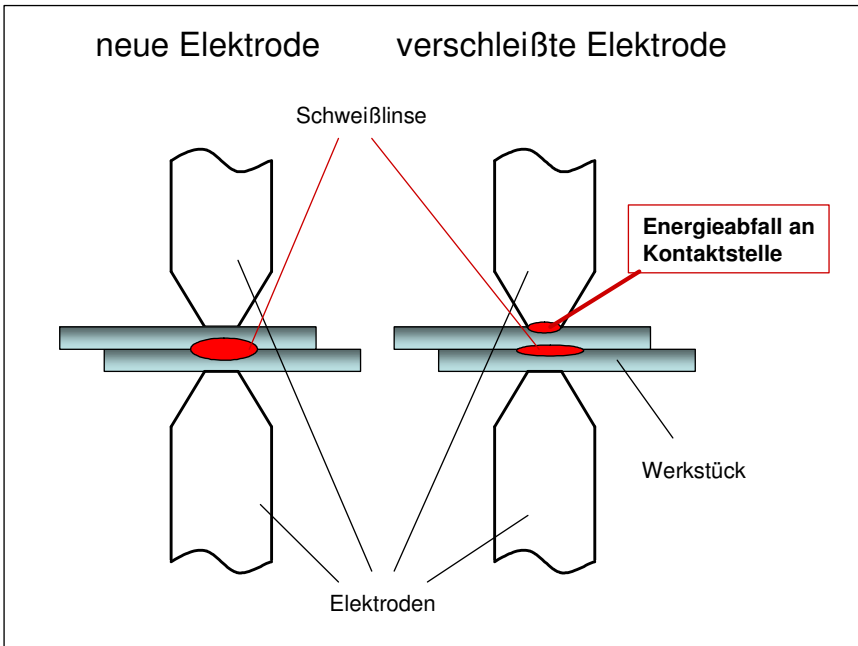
Schemazeichnung Schweißvorgang
